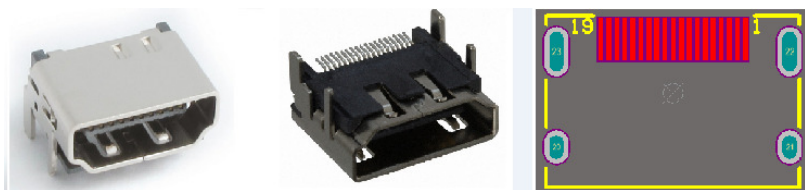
Conector HDMI (vista superior e inferior) e seu footprint.
